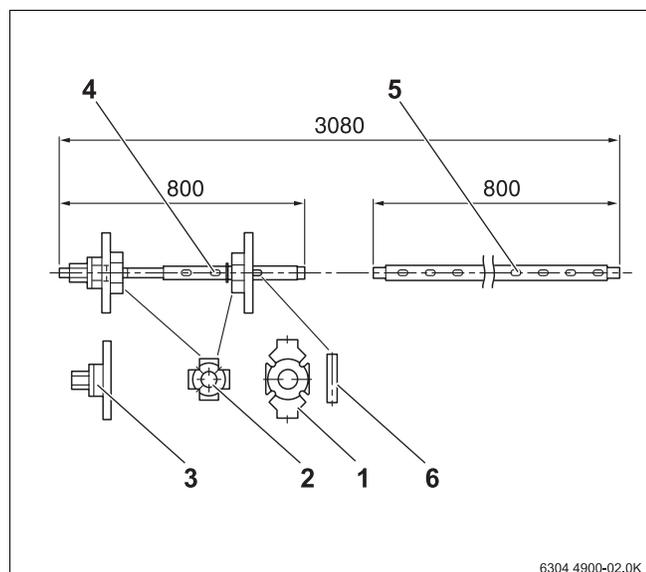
Kesselpresswerkzeug 2.3 (Maße in mm)
